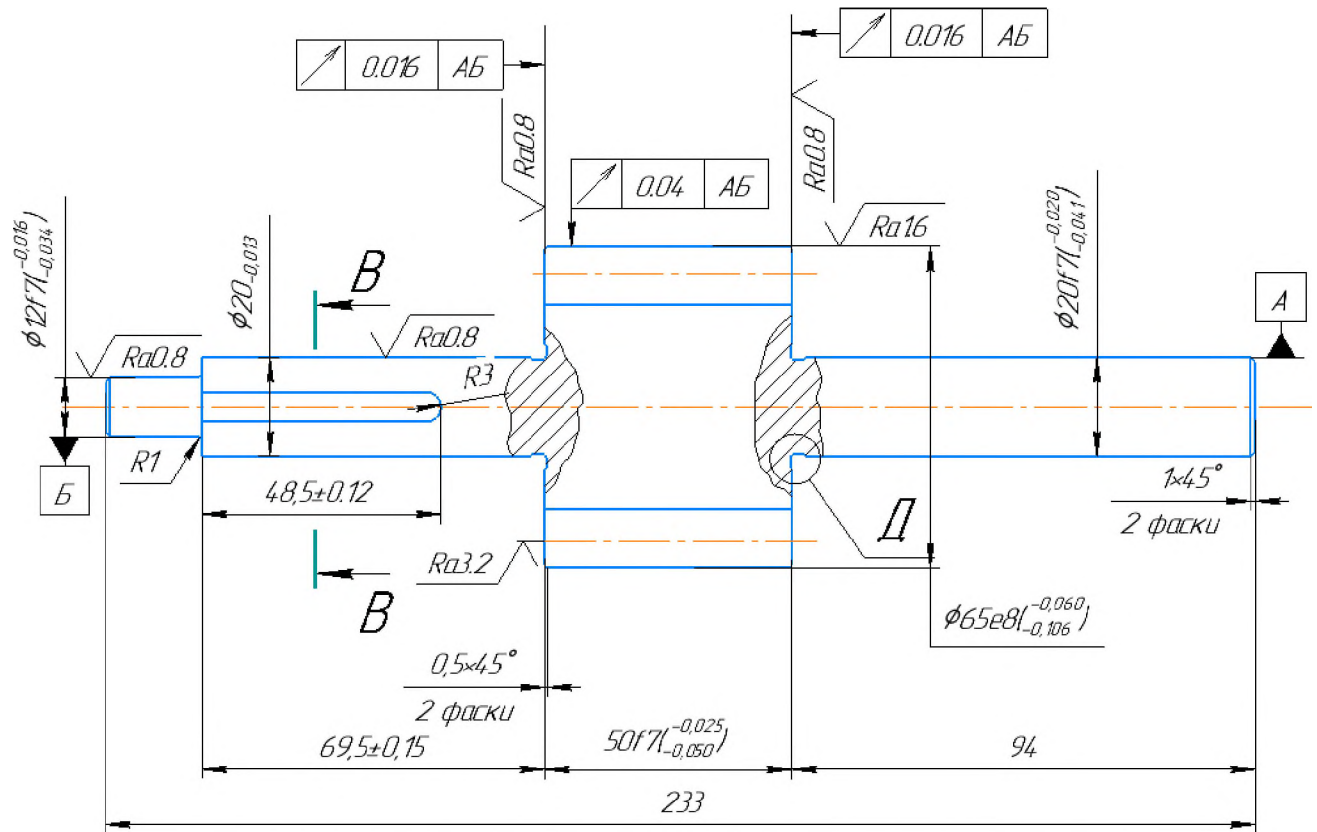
Креслення вала-шестерні шестеренчастого насоса
